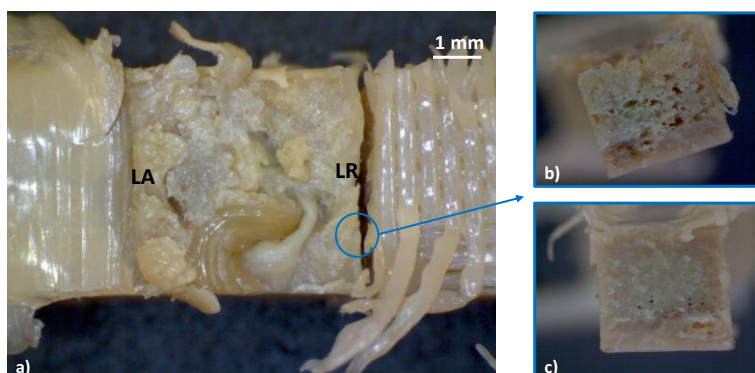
Macrografia do provete após Ensaio 5: a) Superfície superior do provete, b) Superfície de fratura do cordão de soldadura do LR, c) Superfície de fratura da interface do material base com o LR.
